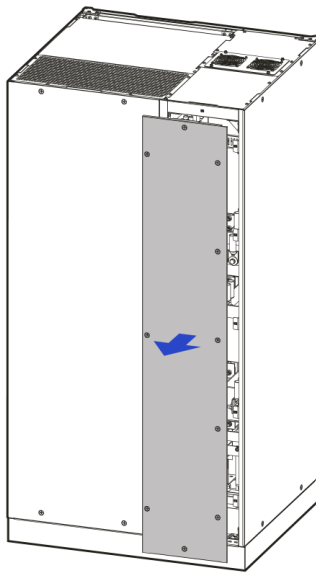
Retiro de la cubierta del cableado del UPS-IND HF 13300 y 13400
